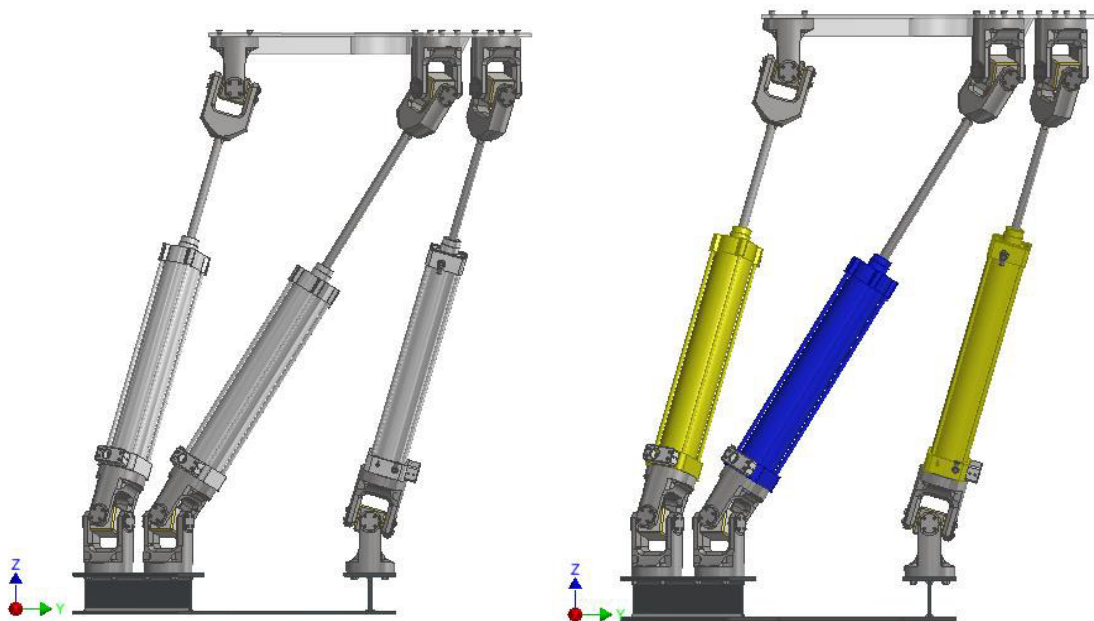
Desplazamiento en el eje Y de la plataforma Stewart-Gough (Vista de plano YZ)
